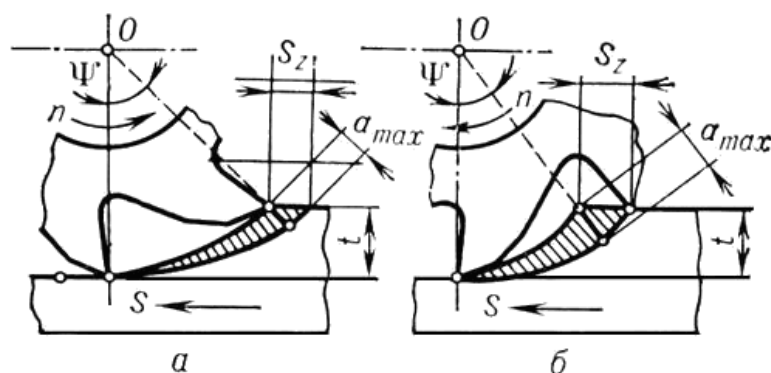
Элементы режима резания и параметры сечения срезаемого слоя при фрезеровании цилиндрическими фрезами
